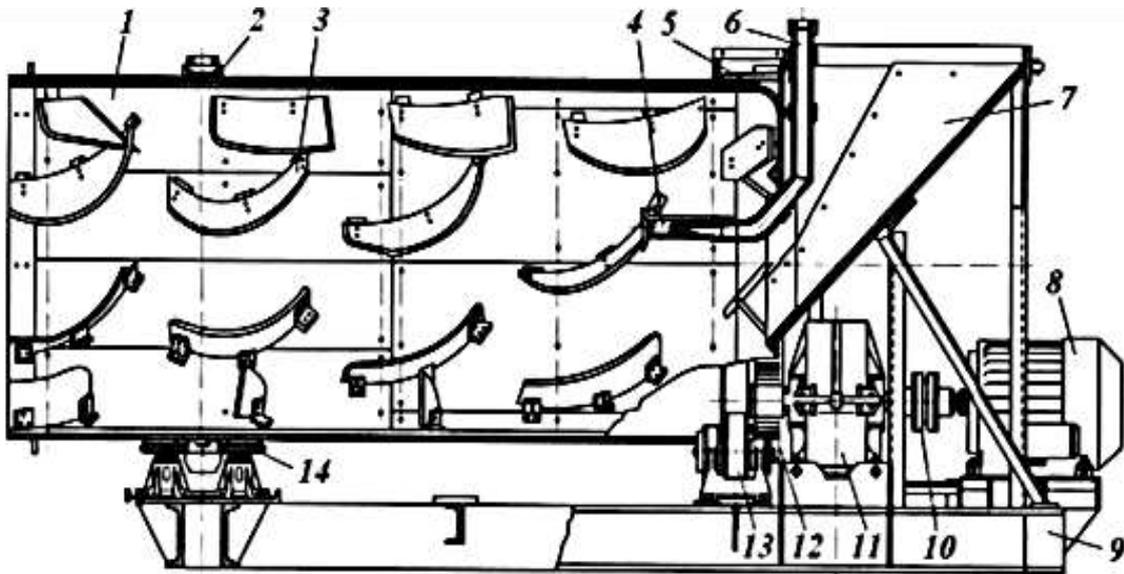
Гравитационный смеситель непрерывного действия: 1-барабан; 2-бандаж; 3-лопасть; 4-водная форсунка; 5-зубчатый венец привода барабана; 6-труба; 7-загрузочная воронка; 8-двигатель; 9-рама; 10-соединительная муфта; 11-редуктор; 12-ведущая шестерня; 13-опорный ролик; 14-упорный ролик.
